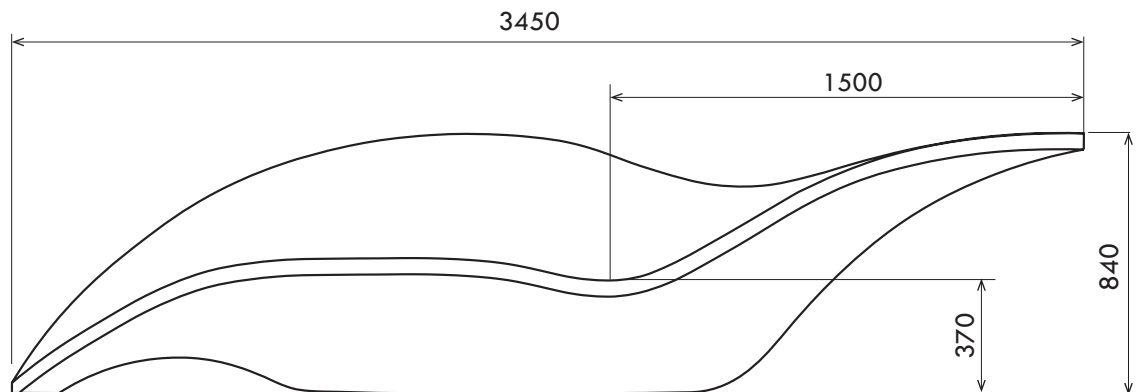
Medidas generales del diseño, relevantes para la posición tumbada
